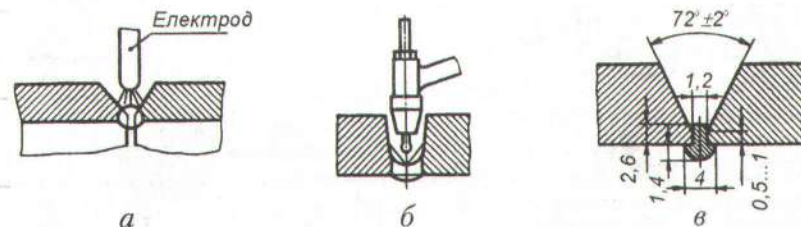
Способи зварювання кореневого шару «на вазі»:
